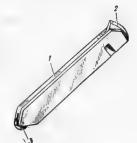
1 — корпус; 2 — нож; 3 — ролик
